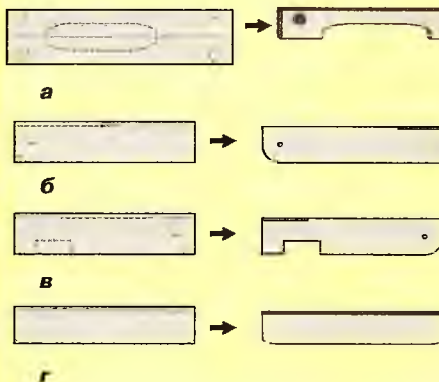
Детали леткового заградителя: а — корпус; б — глухая и в — ограничительная поворотные заслонки; г — передвижная заслонка
